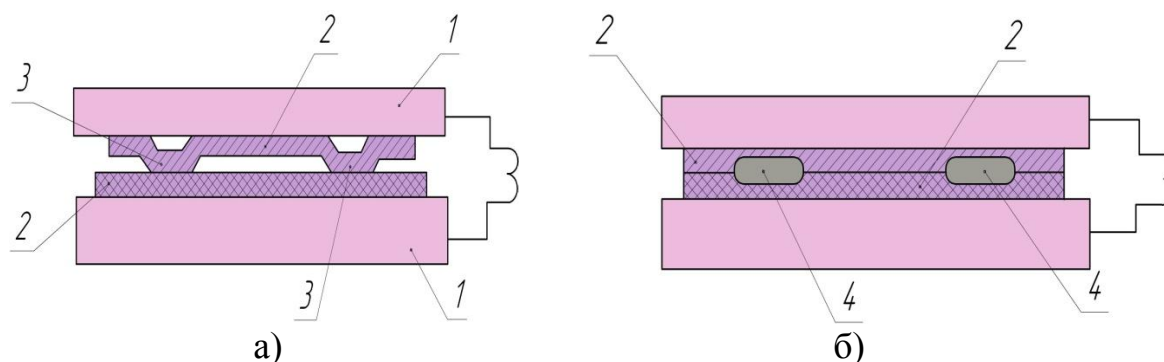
Схема рельефной сварки: а – до сварки; б – после сварки;
